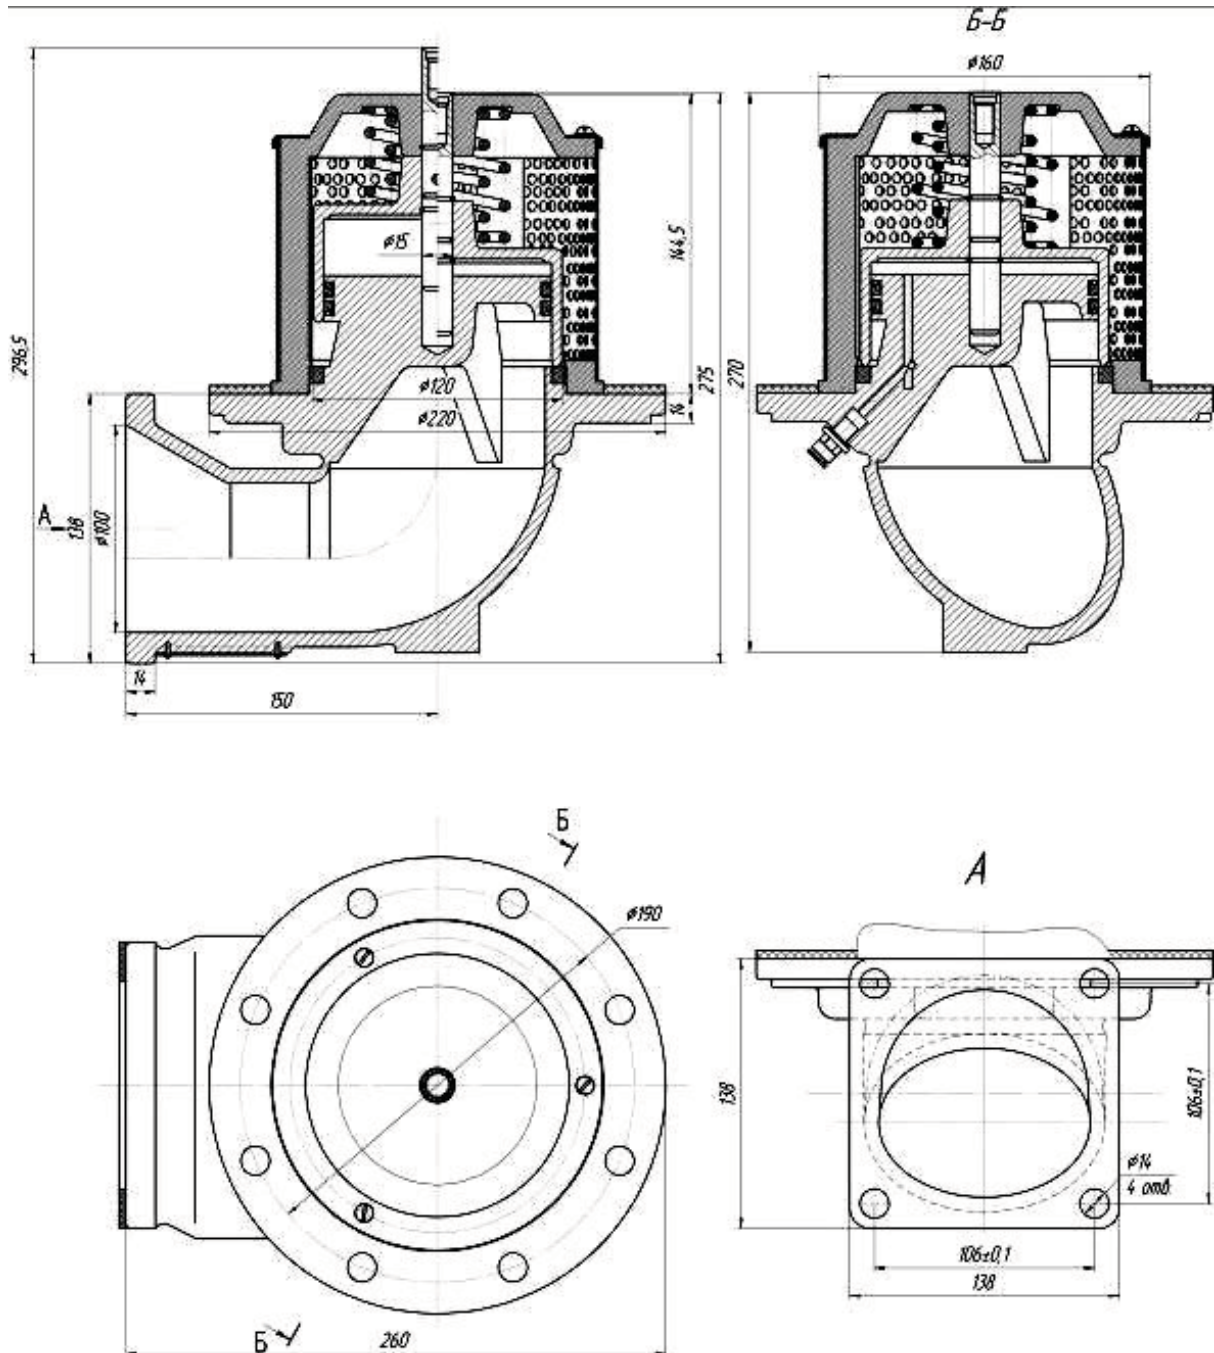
Типовой представитель: клапан донный пневматический низкий профиль
